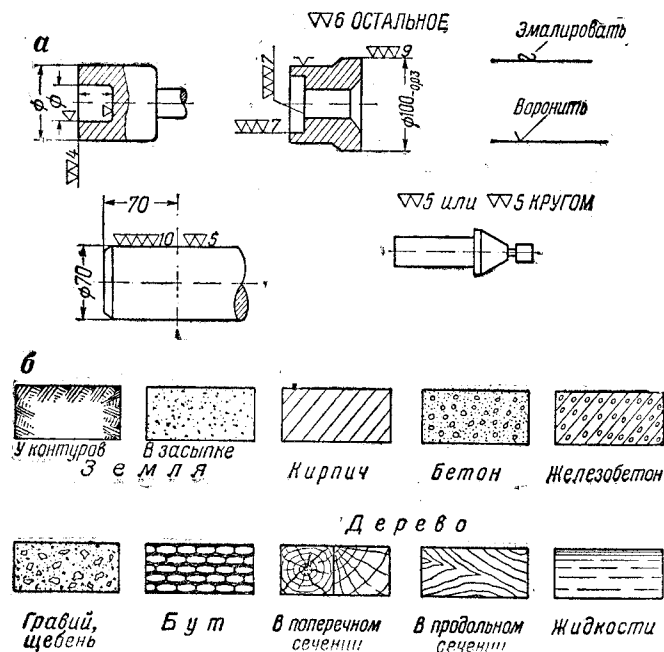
Условные обозначения на чертежах: а — обозначения обработки поверхностей деталей; б — обозначения материалов в разрезах и сечениях
